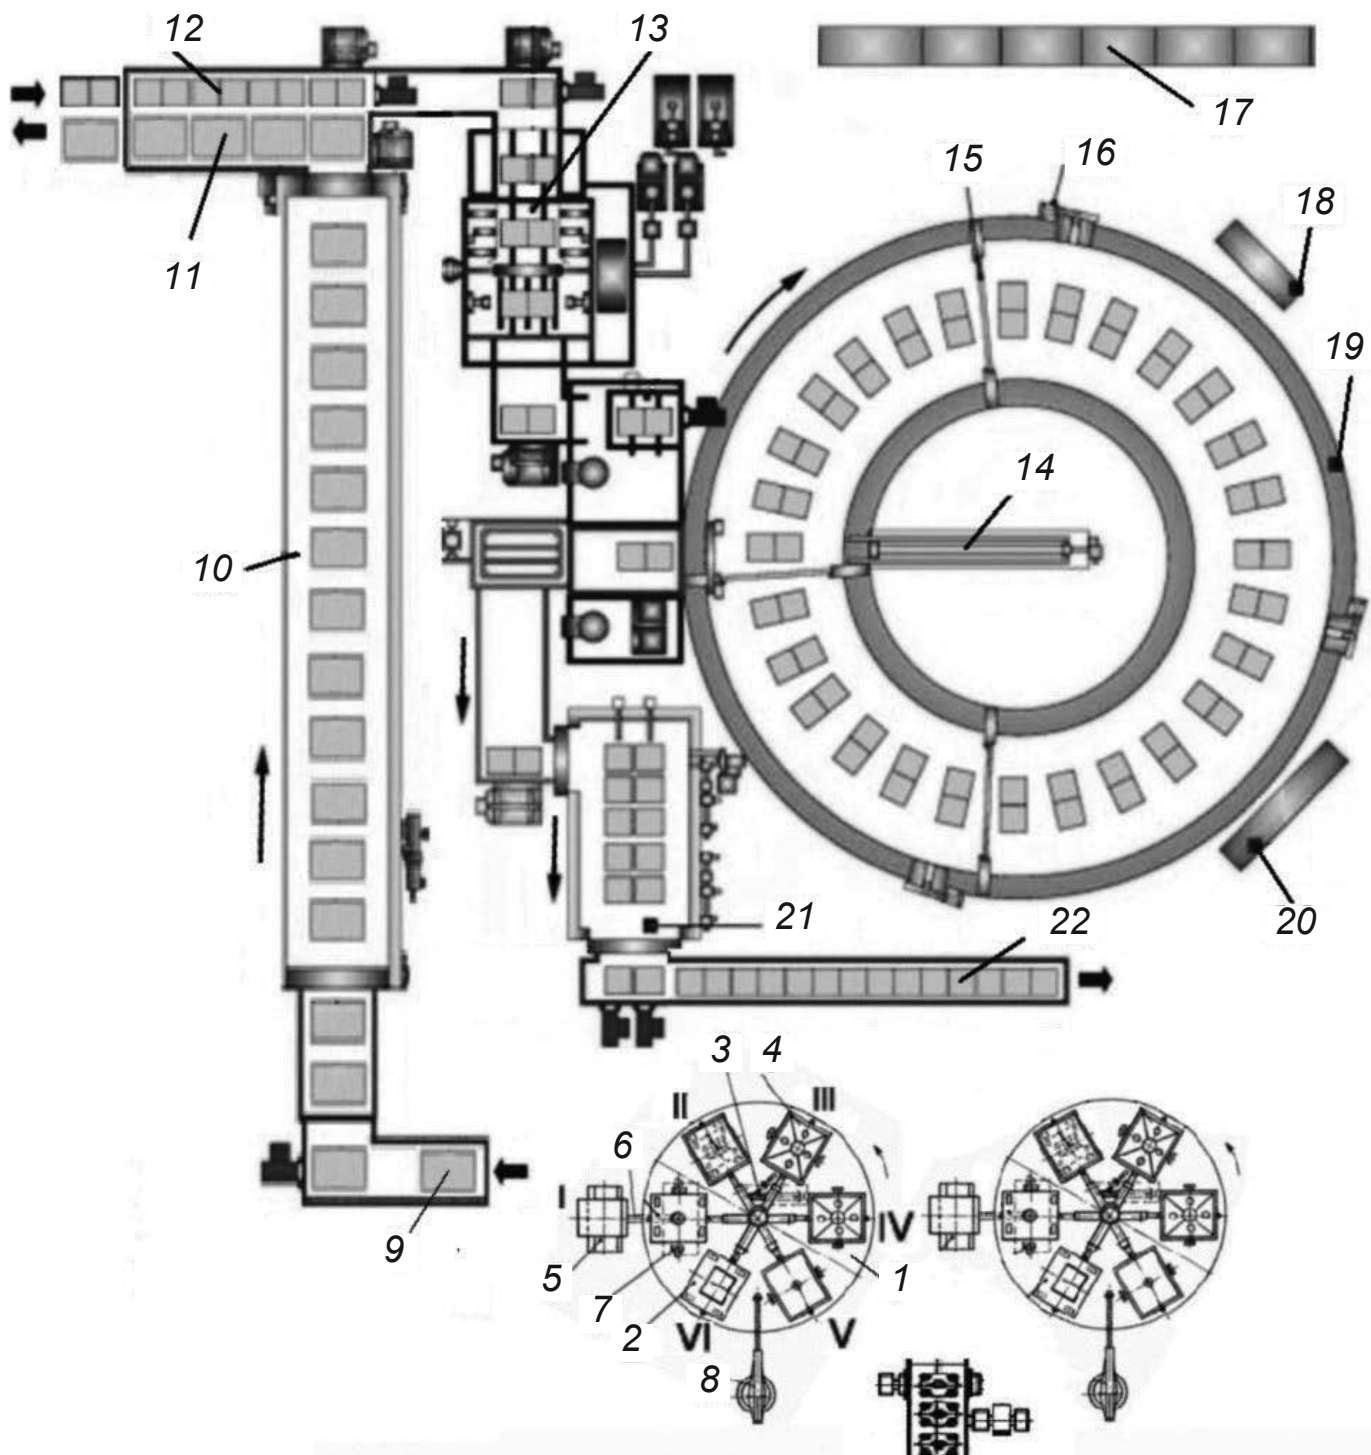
Схема РКК с двумя роторными формовочными модулями и кольцевой термической печью непрерывного действия
